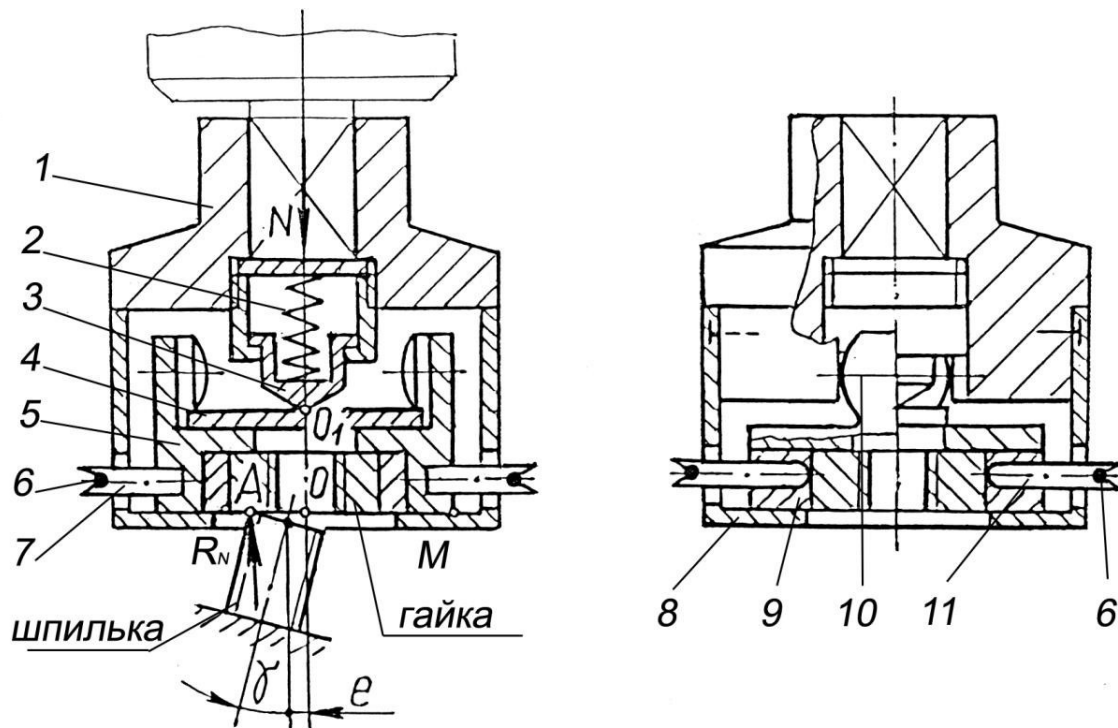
Головка з податливим базуванням гайки: 1- корпус; 2- осьова пружина; 3- втулка; 4- шайба проміжна; 5- напрямна бази гайки; 6 – кільце пружинне; 7, 11 – штифти; 8 – обмежувальна втулка; 9 – база гайки; 10 – заокруглені виступи напрямної 5.
